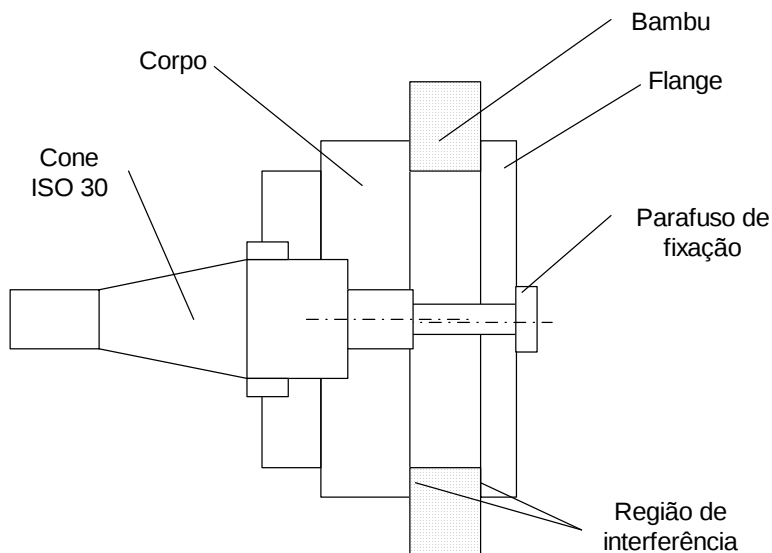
Suporte para fixação no dispositivo laminador.
